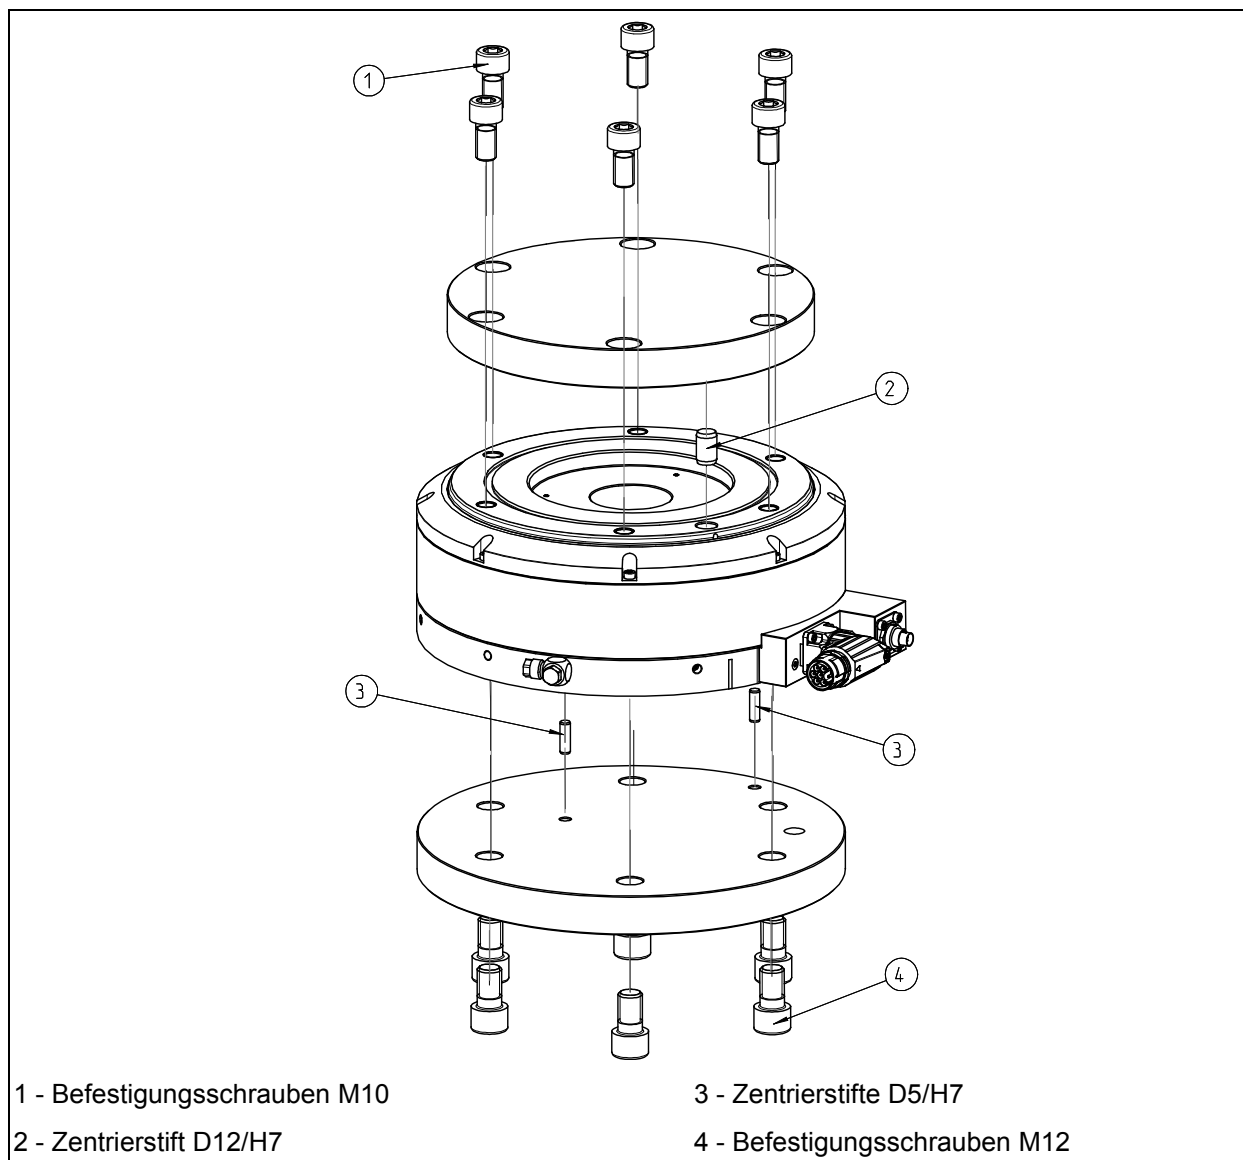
Ansicht Montage der Adapterplatten am Rotor und Grundträger
